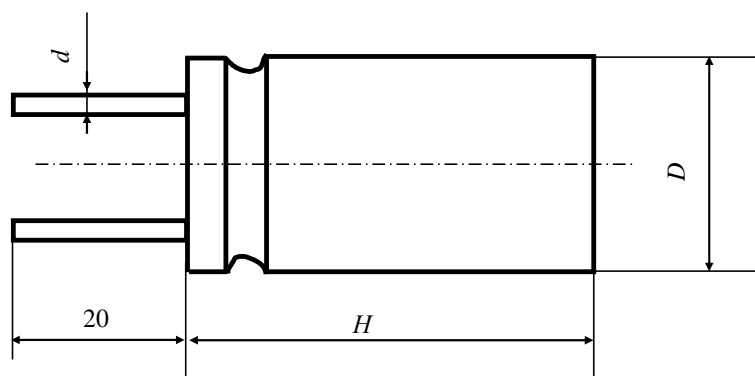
Внешний вид и габаритные размеры электролитического конденсатора К50-16
